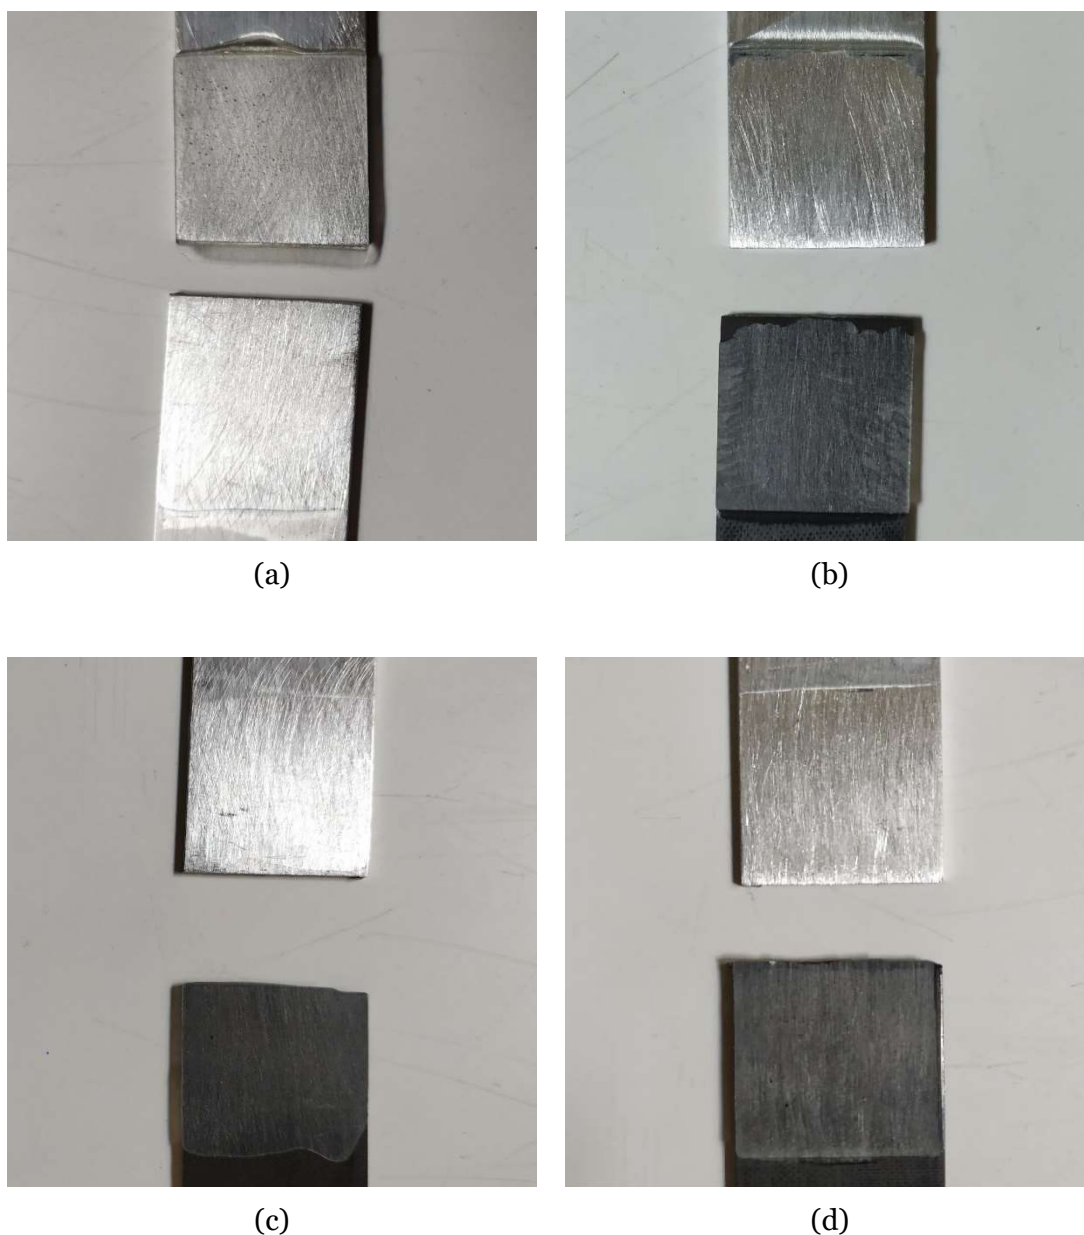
Macroscopia ótica às superfícies de falha das juntas de sobreposição simples com comprimentos de sobreposição de 25mm.
